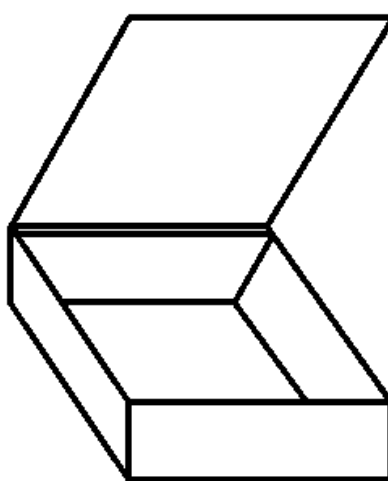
Эскиз корпуса с крышкой без отбортовок
